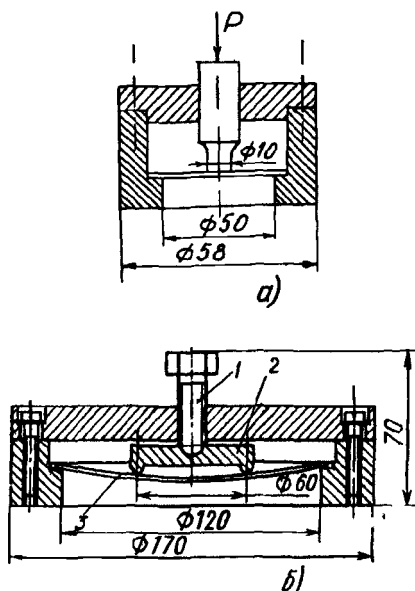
Приспособления для нагружения малогабаритных дисковых образцов на двухосный изгиб
